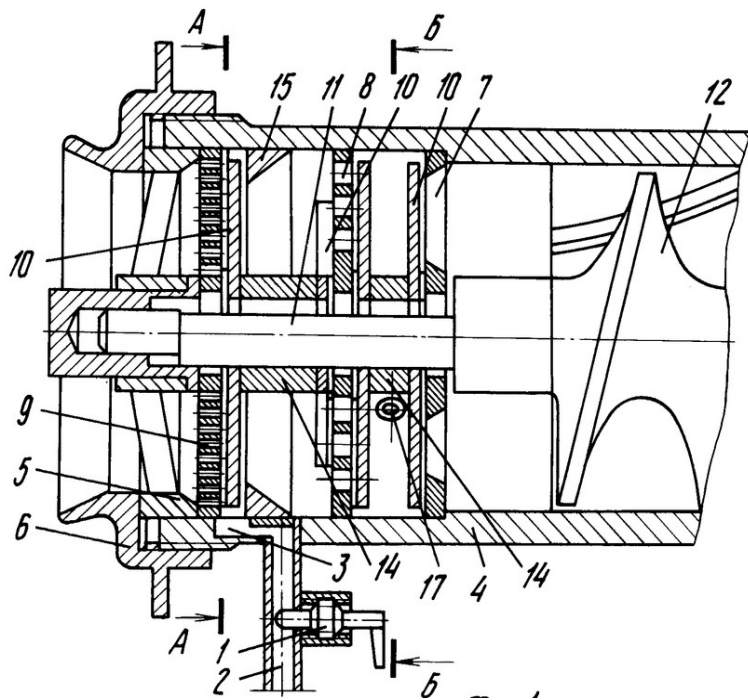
Продольный разрез режущего узла волчка с периферийной выгрузкой улавливаемых включений
